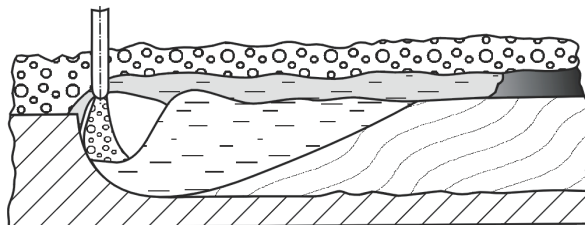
Схема процесса сварки под флюсом [2]
